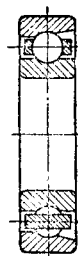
Опорные шарикоподшипники с плоскими шайбами
